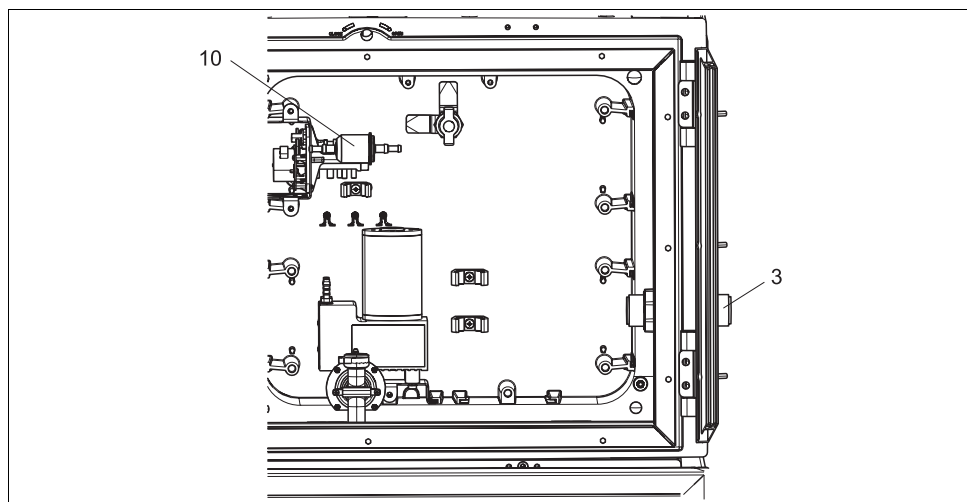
Parti di ricambio per la versione con pompa per vuoto (vista dietro al supporto della pompa)
